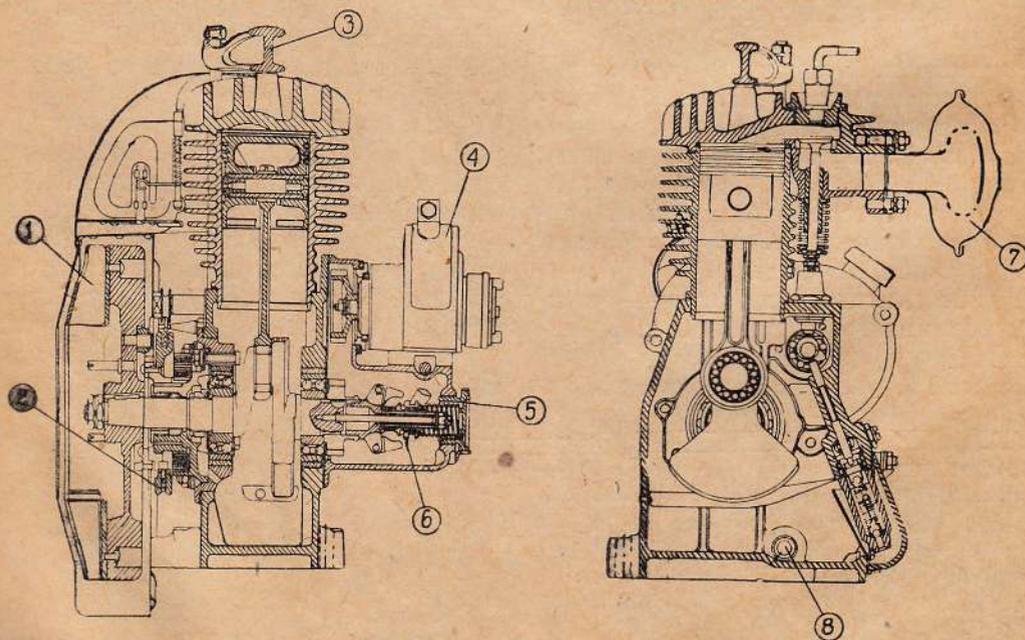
Разрез двигателя: 1 — вентилятор, 2 — пусковой механизм, 3 — траверс крепления головки цилиндра, 4 — магнето зажигания, 5 — регулировочная гайка регулятора, 6 — регулятор числа оборотов, 7 — шатун, 8 — спускная пробка для масла из картера двигателя.
